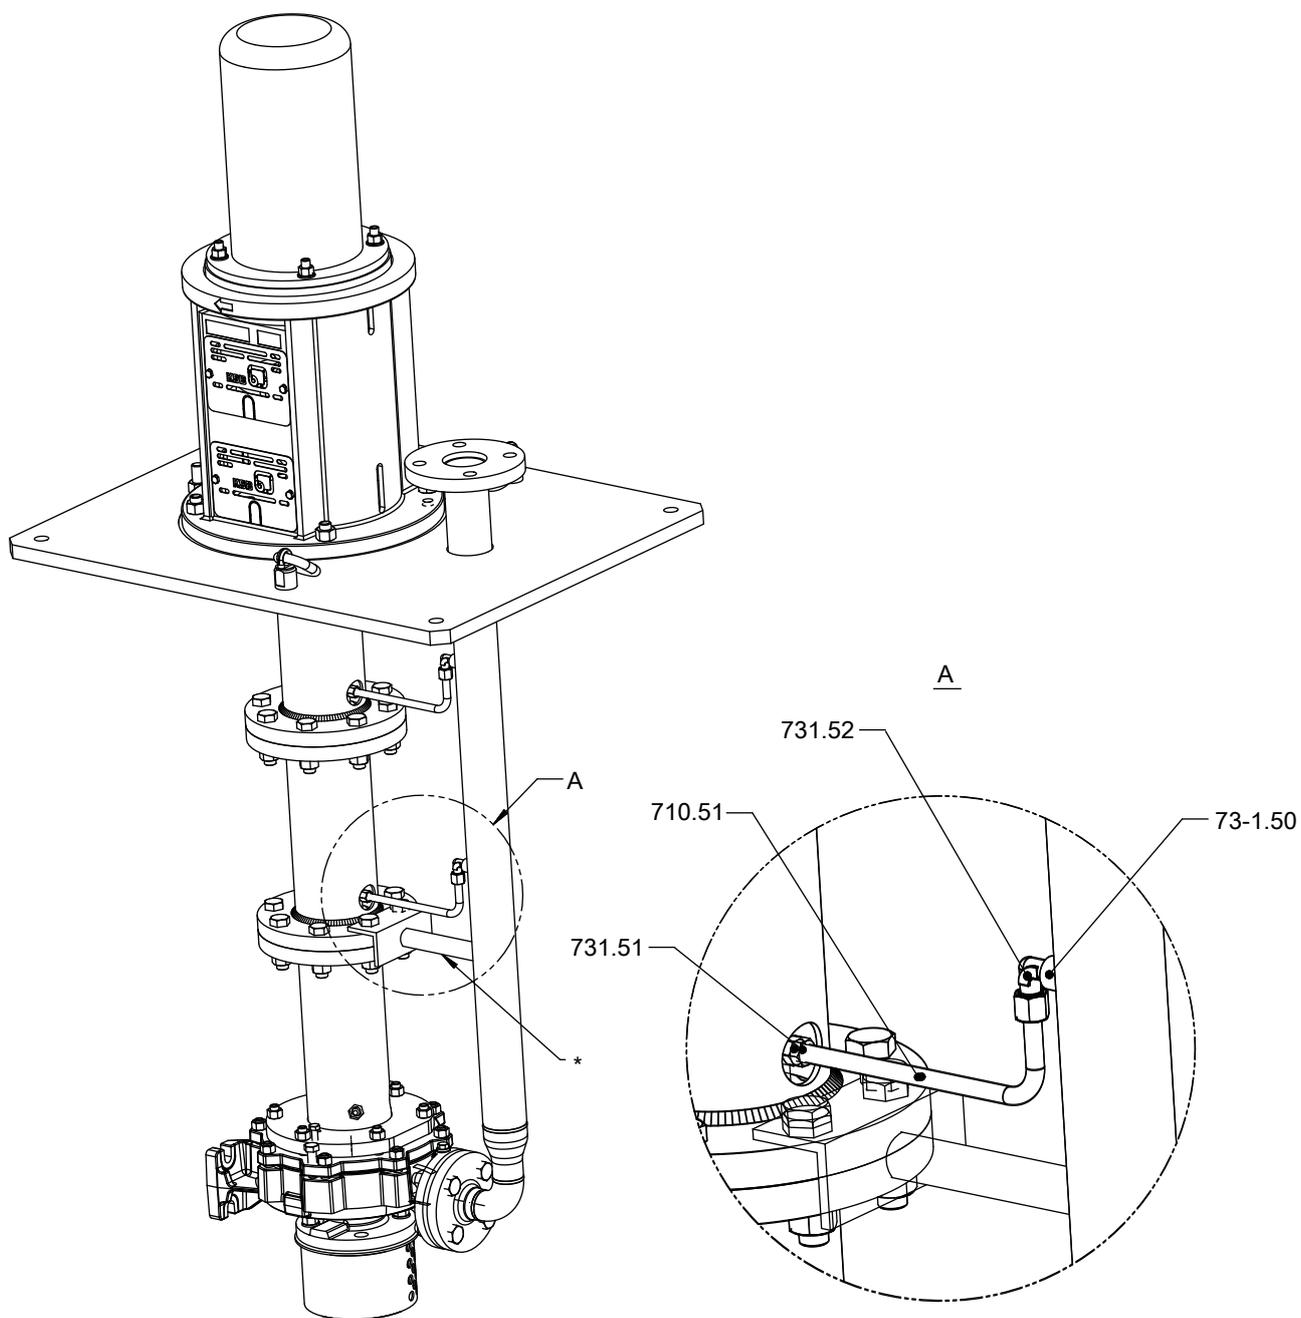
Detailzeichnung Schmierung mit Fördermedium
